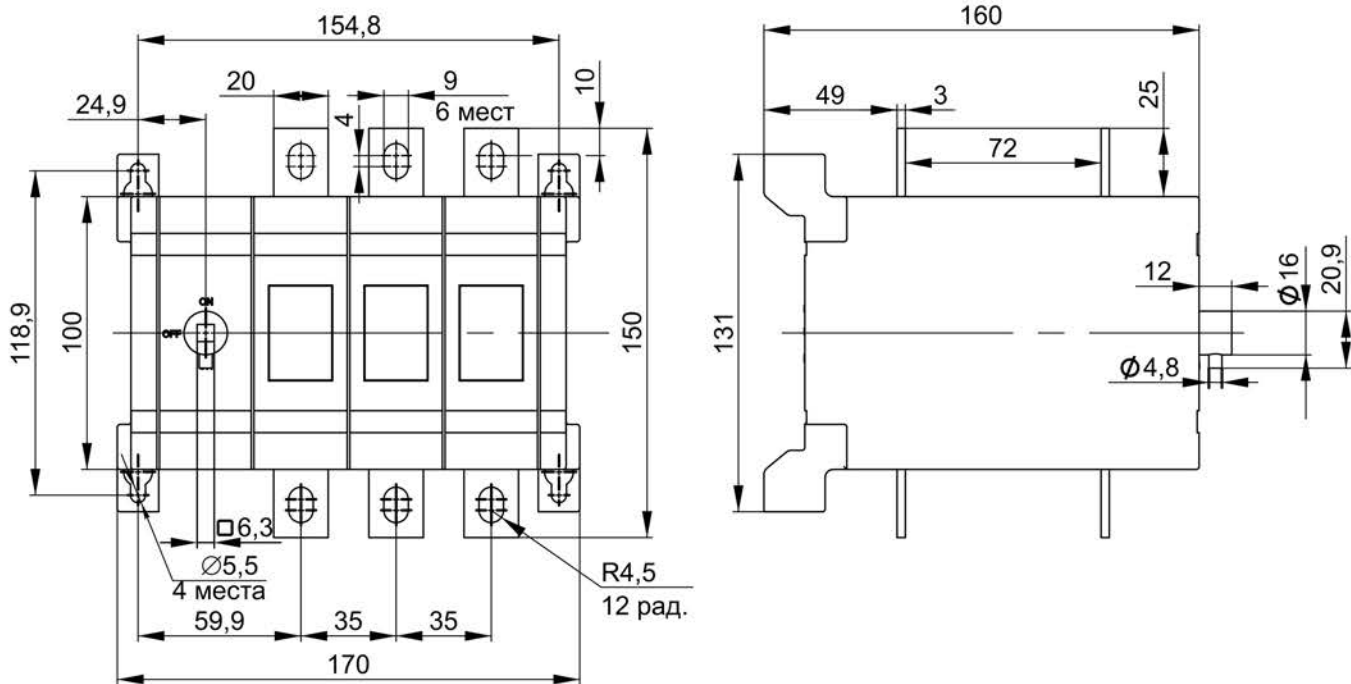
Габаритные, установочные и присоединительные размеры реверсивных ВРК 160–250 А / Figure 5 – Overall, mounting and connection dimensions of reverse VRK 160–250 A
